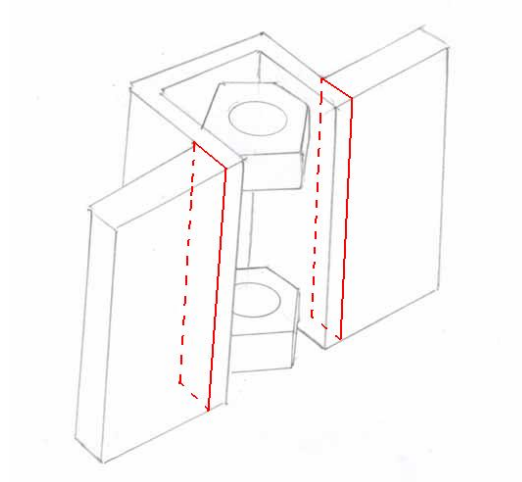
Vista de la soldadura en la guía del husillo
